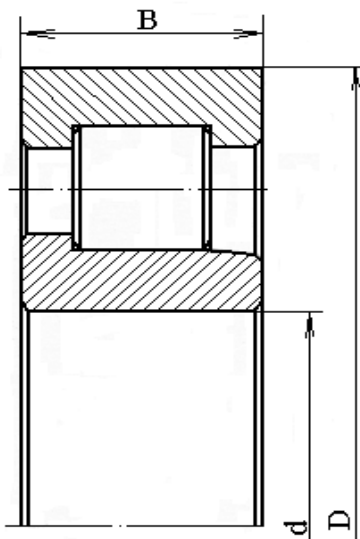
Подшипник роликовый радиальный, с короткими цилиндрическими роликами
